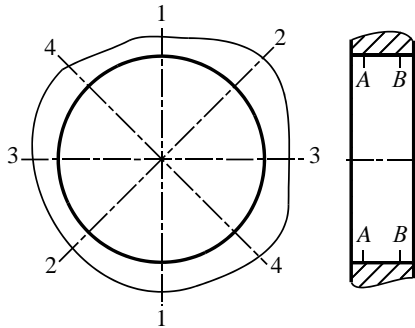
Схема вимірювання отворів корпусних деталей:
